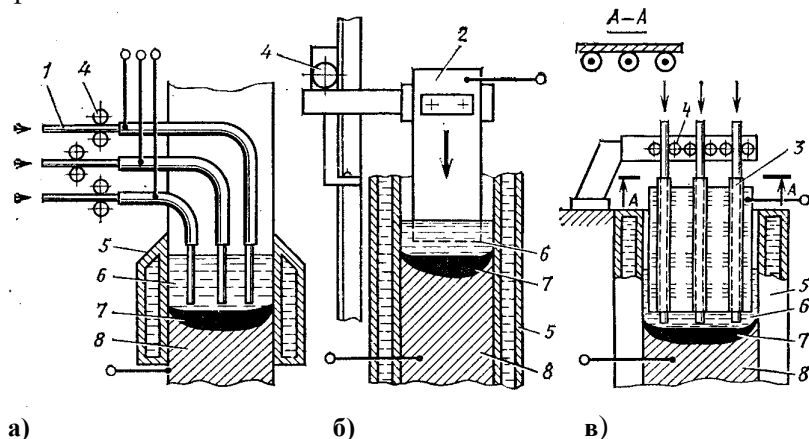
Способы электрошлаковой сварки:
